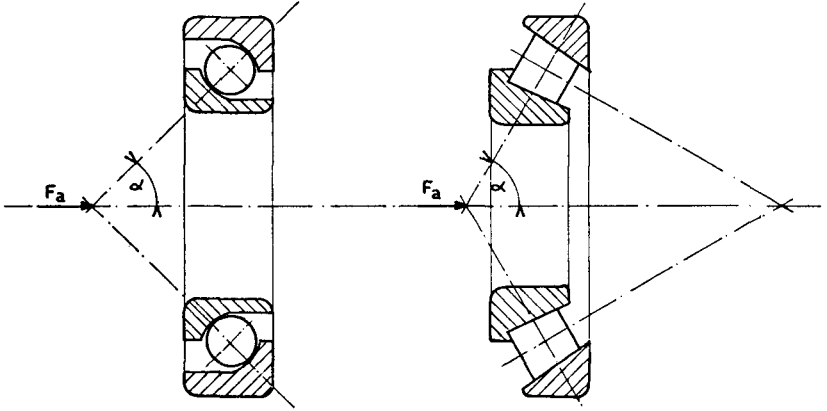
Roulement à billes à contact oblique et roulement à galets côniques soumis à une charge axiale.
